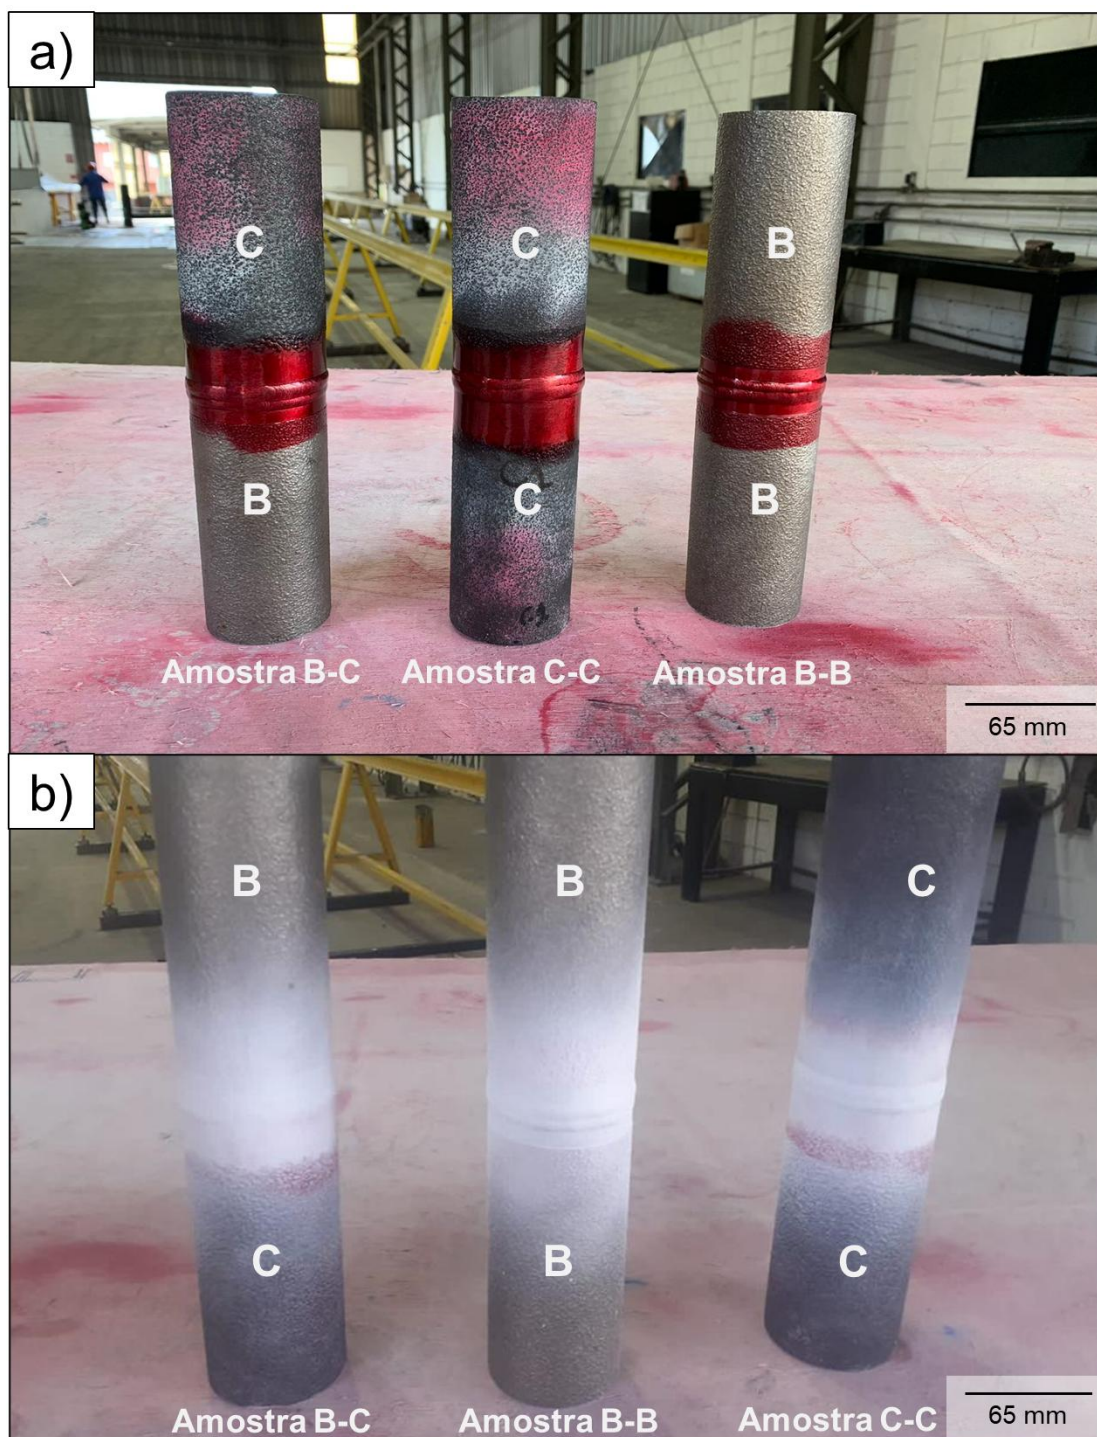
Ensaio de líquido penetrante. Amostras soldadas (a) com o líquido e (b) o revelador aplicado na região da solda.
